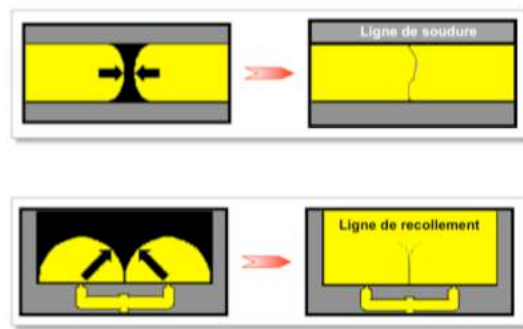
Tipos de línea de soldadura. Fuente: ECL
